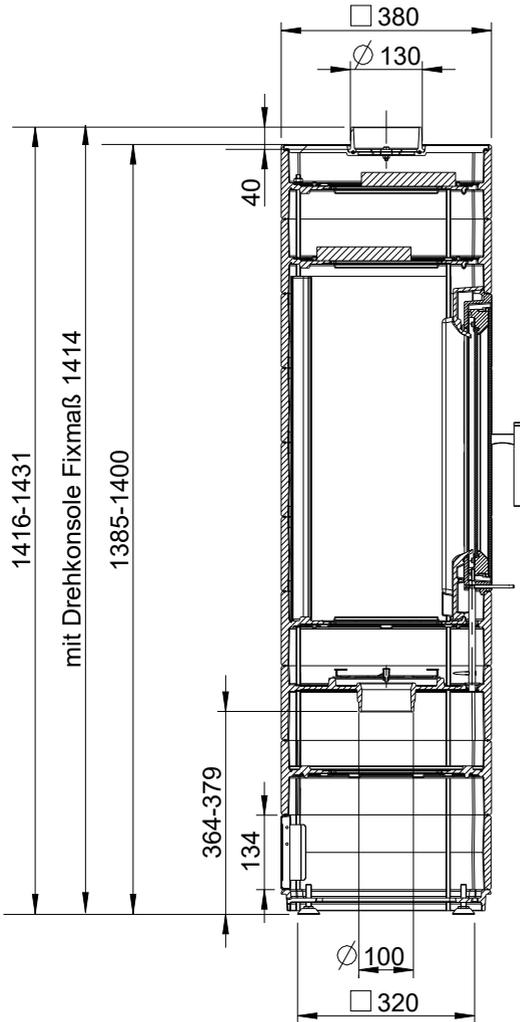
Sortie des fumées, dimensions pour une buse raccordée vers le haut- CORNA hochaut, CORNA hochaut tec ou CORNA hoch ES
